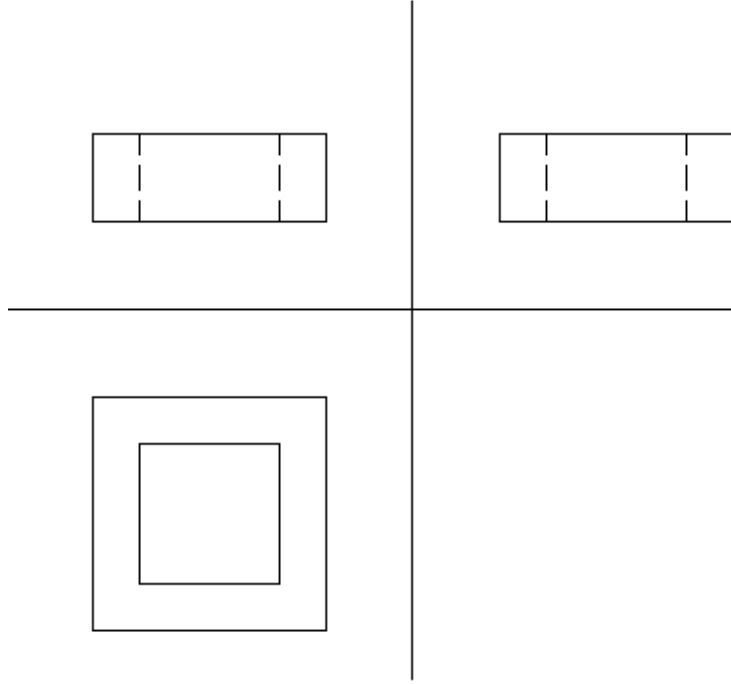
Temel boyutların profil düzlemine taşınması
